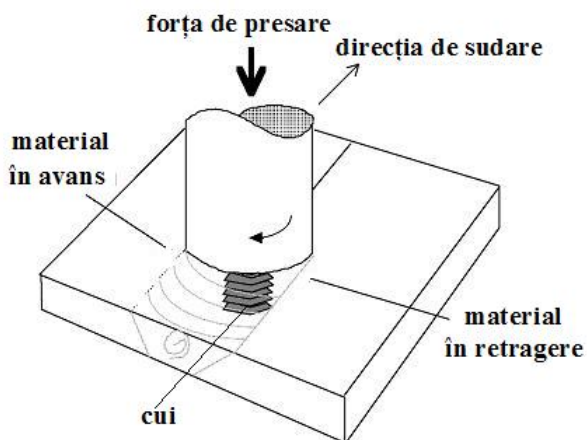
Schema de principiu a sudării prin frecare cu amestecare
